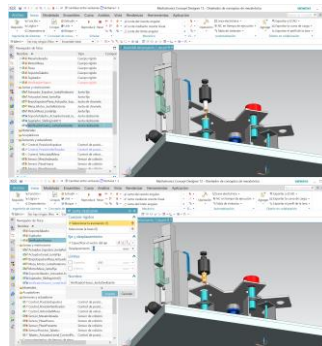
Junta deslizante verificador, con 8 mm de desplazamiento.
